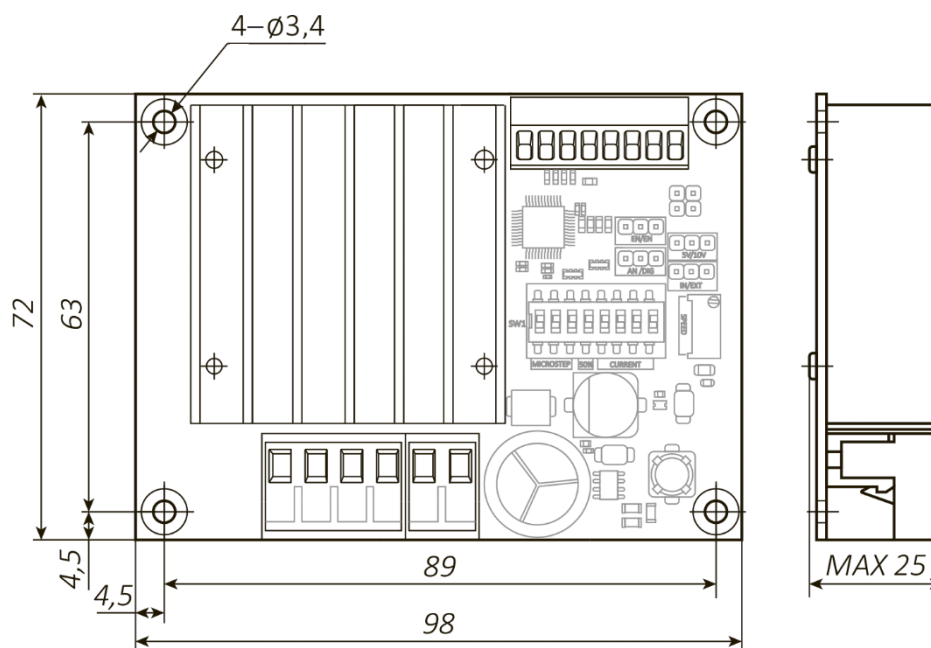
Dimensiones del controlador RS 206411 del motor paso a paso
